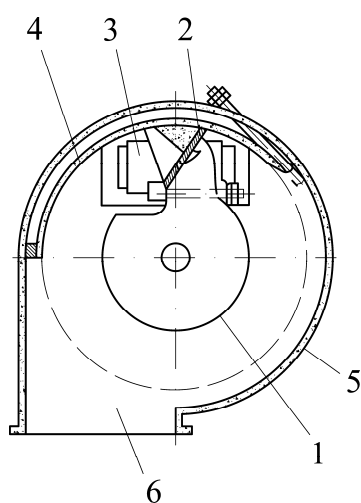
Схема метательной головки центробежного пескомета: 1 – ротор; 2 – сменная лопатка или ковш; 3 – ленточный конвейер, подающий в головку формовочную смесь; 4 – направляющая дуга; 5 – кожух головки; 6 – выходной патрубок кожуха
